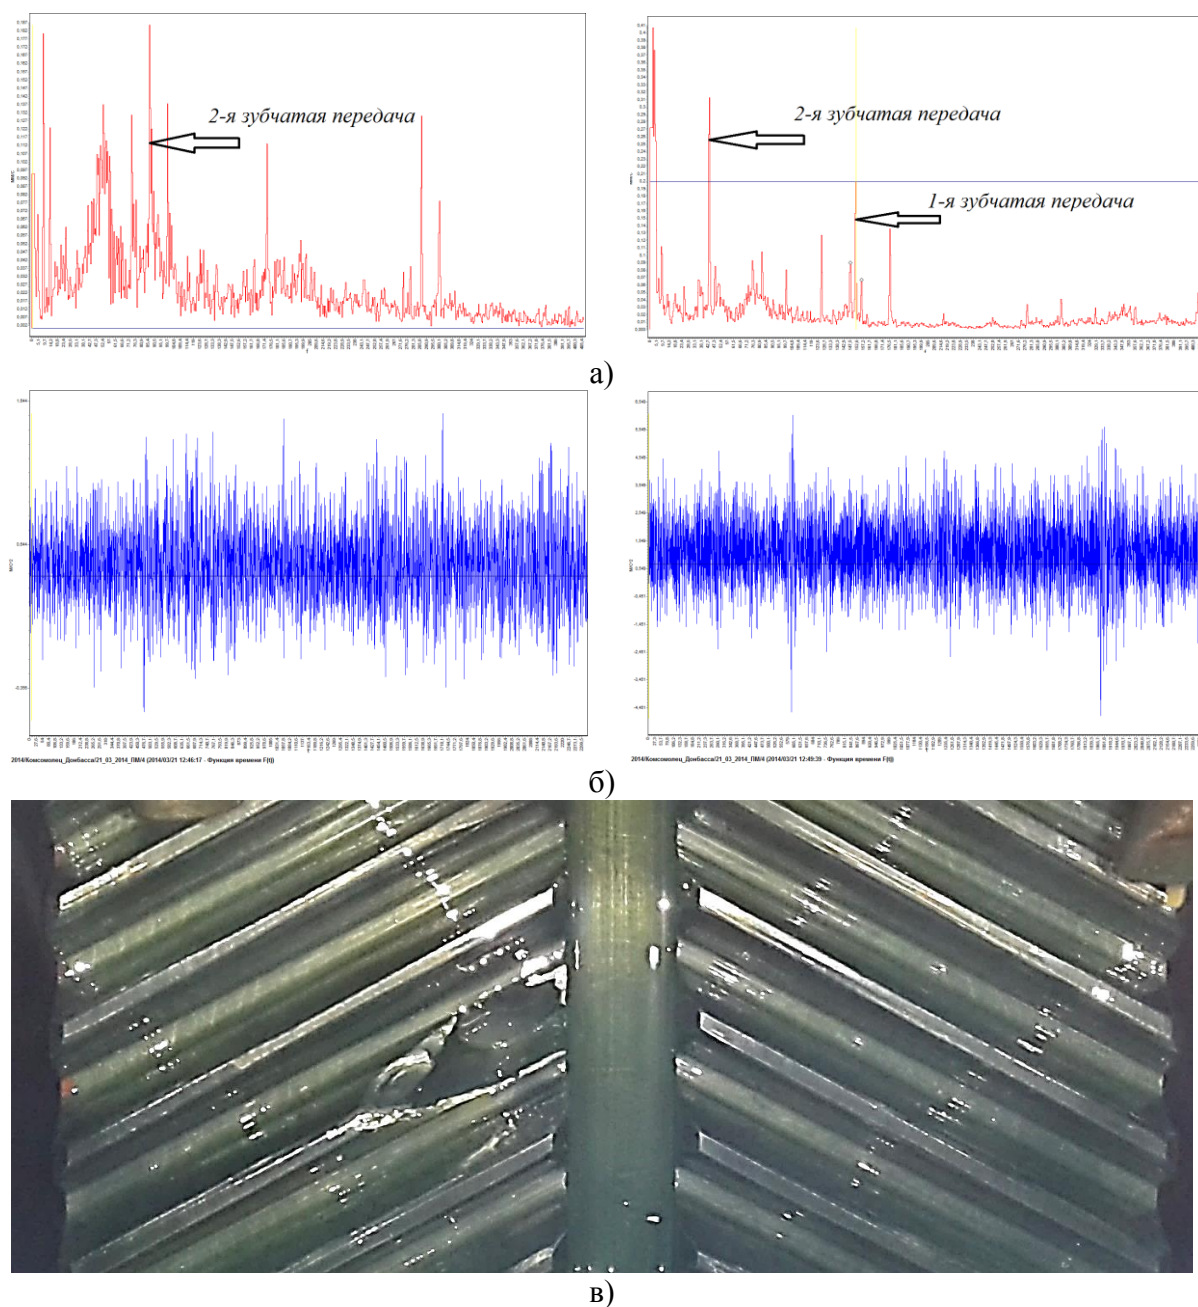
Диагностирование скола зуба колеса тихоходной передачи привода редуктора машины шахтного подъёма:
